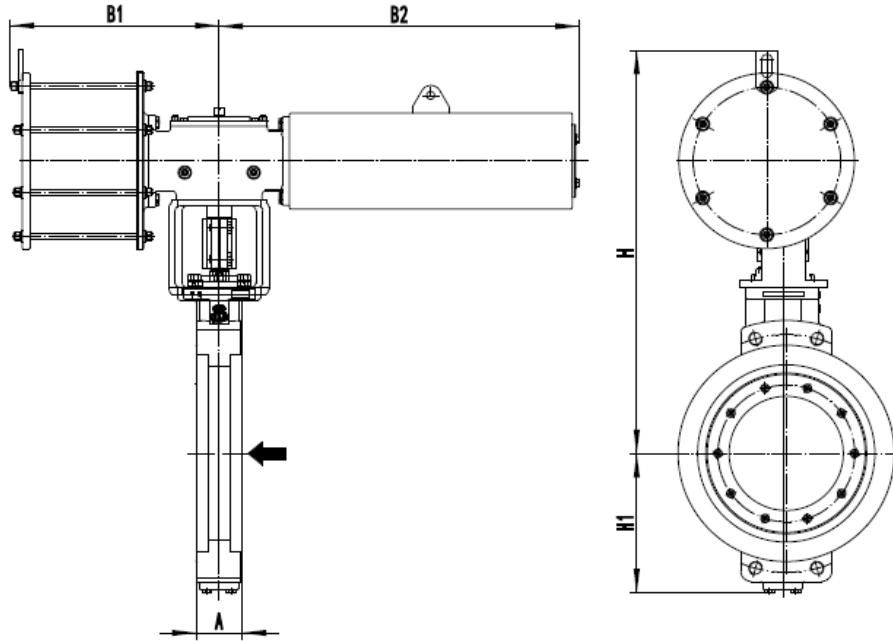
配 AW18SR41~AW85SR56 外形尺寸图 (FC)
